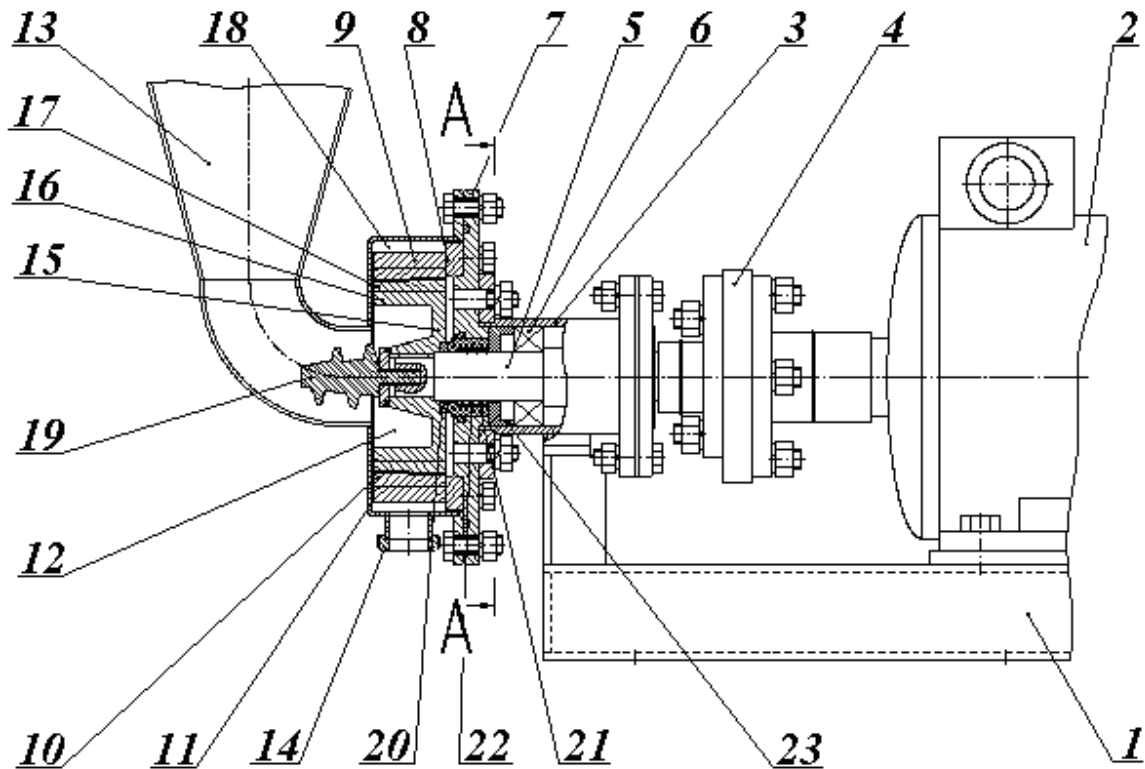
Схема загального вигляду лабораторного подрібнювача м'ясної сировини Я5-ФПФ: 1) рама; 2) електродвигун; 3) корпус; 4) пружна муфта; 5) робочий вал; 6) підшипникові опори; 7) опорний фланець; 8) статор; 9) зубці статора; 10) накладки на зубцях статора; 11) кришка; 12) робоча камера; 13) бункер; 14) патрубок; 15) ротор; 16) різальні зубці ротора; 17) накладки на зубцях ротора; 18) кільцевий канал; 19) шнек; 20) набір шайб; 21) фторолонова втулка; 22) пружина; 23) притискна шайба.
